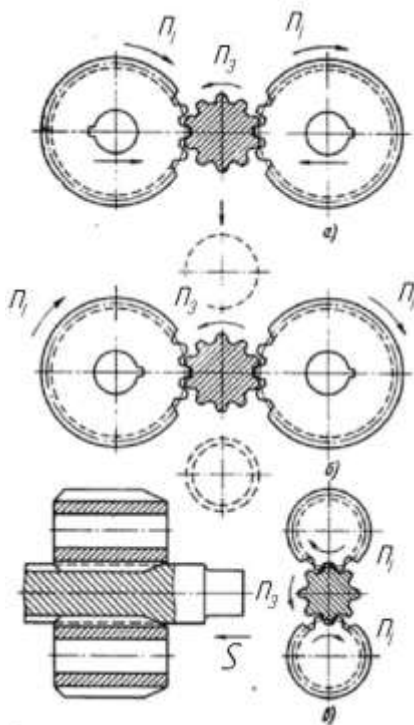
Схема накочування зубів валу круглими зубчастими роликками: *a* – з радіальною подачею роликків; *b* – з тангенціальною подачею заготовки; *в* – з осьювою подачею заготовки;  $n_1$  – напрям обертання інструменту;  $S$  – напрям подачі;  $n_2$  – напрям обертання заготовки
